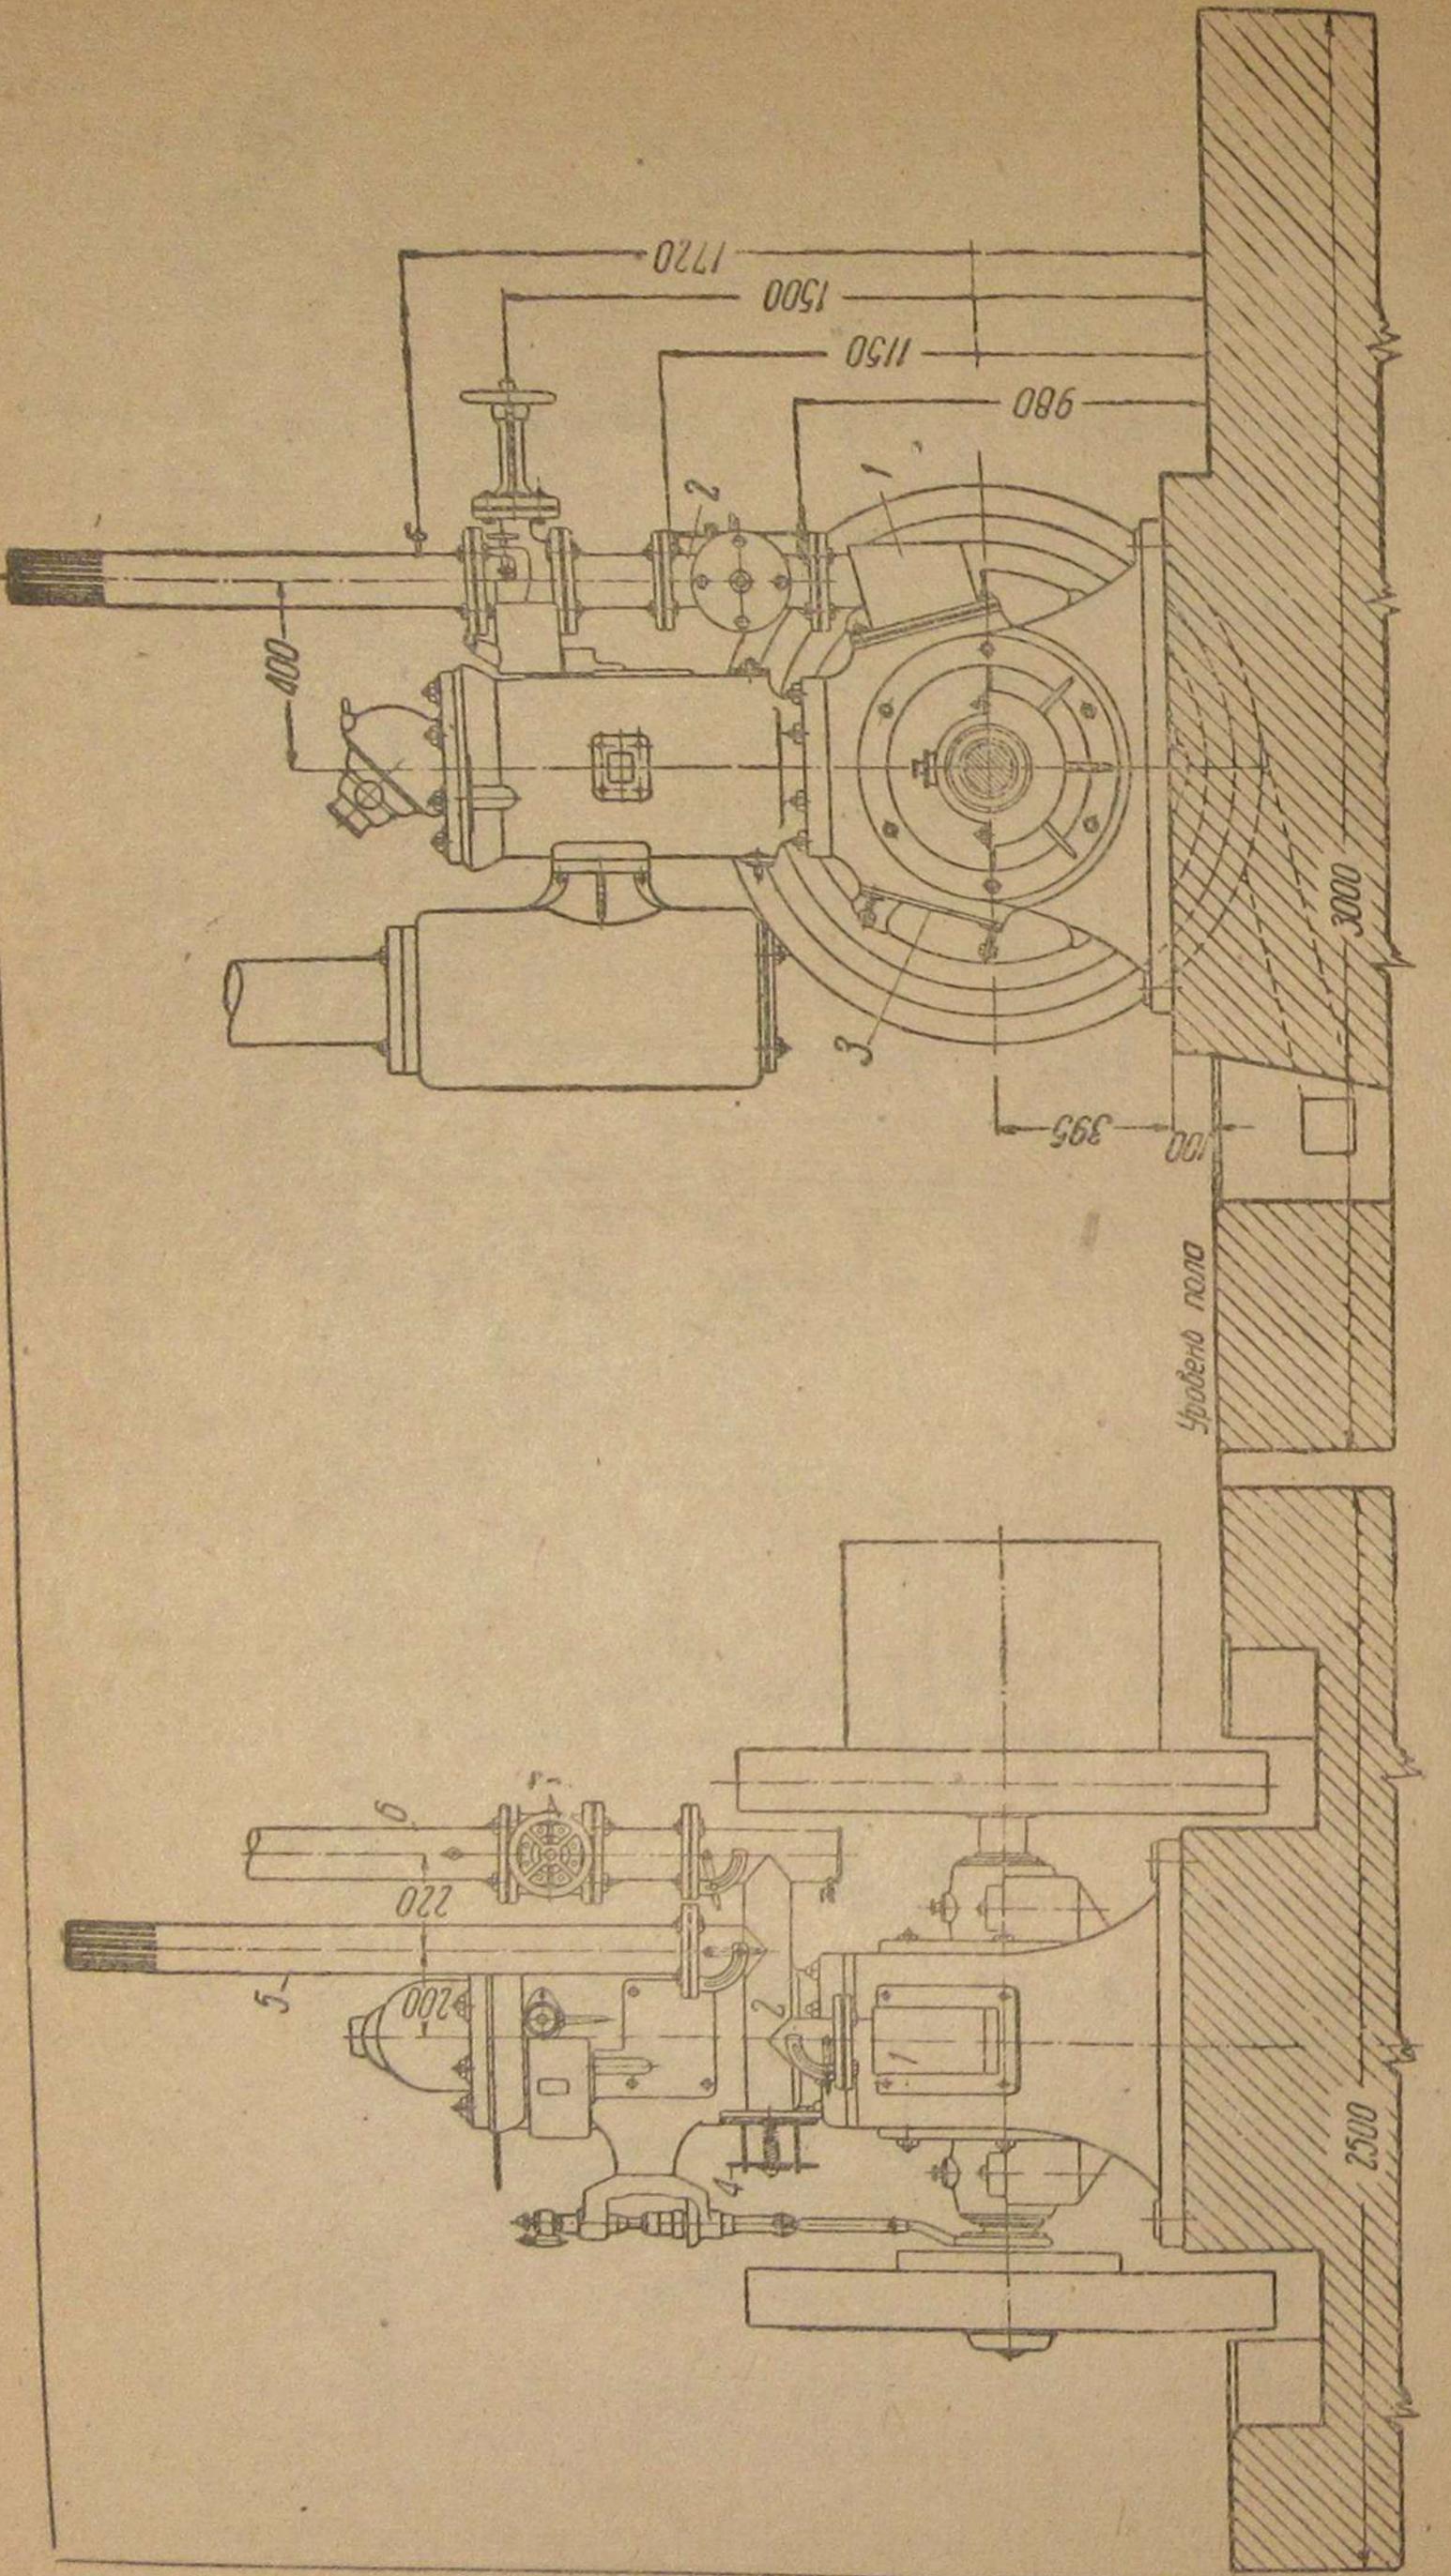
Общий вид двигателя ДВ-35 (переведённого на газ):
